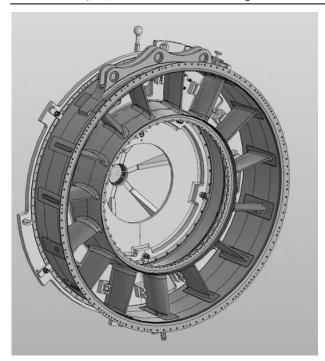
Сборочно-сварочное приспособление без прижимов
